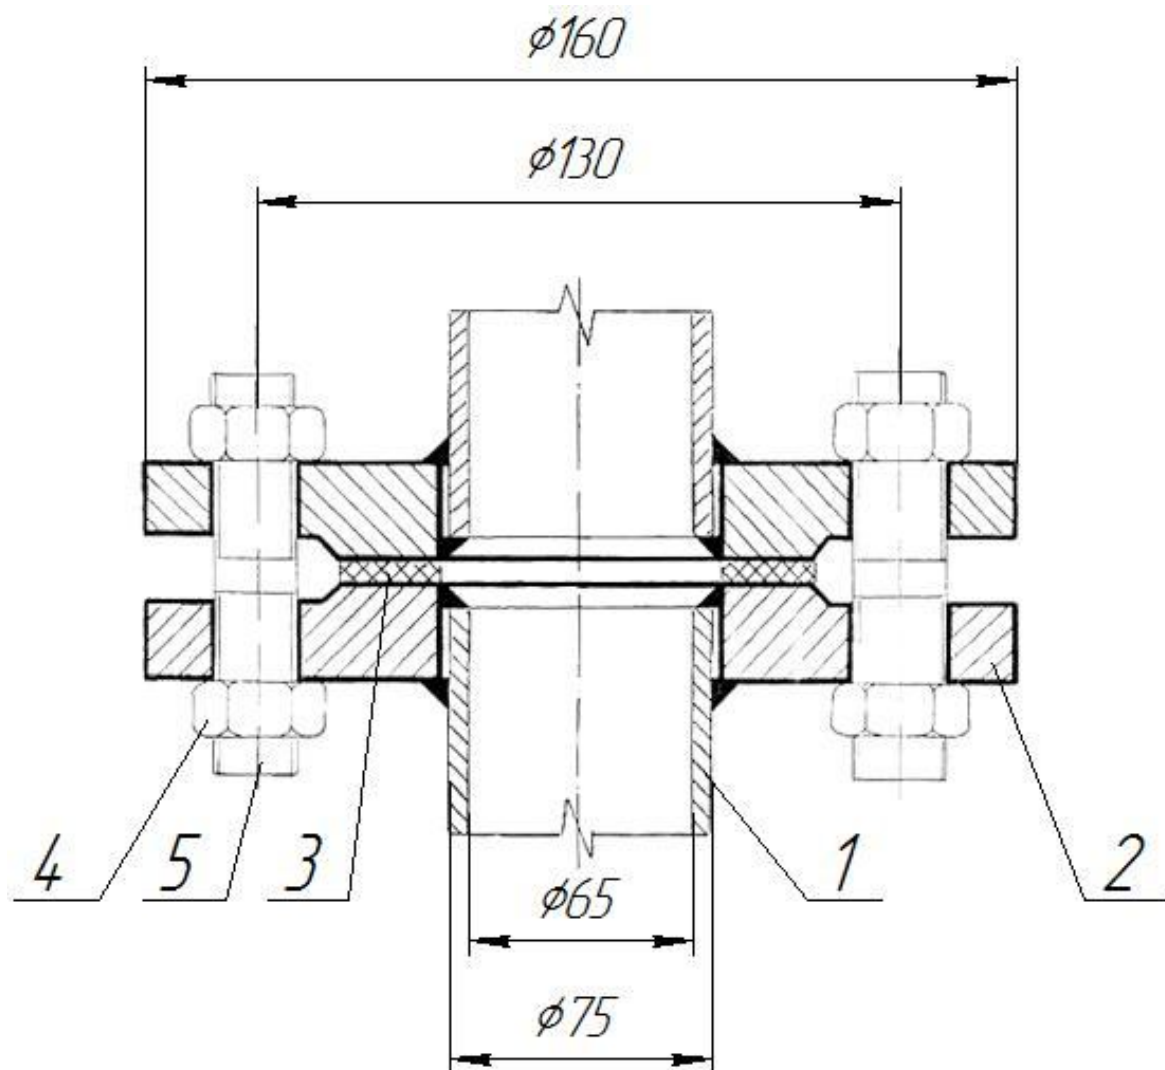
Конструкция фланцевого соединения. 1-труба; 2-фланец; 3-прокладка; 4-гайка; 5-шпилька.
